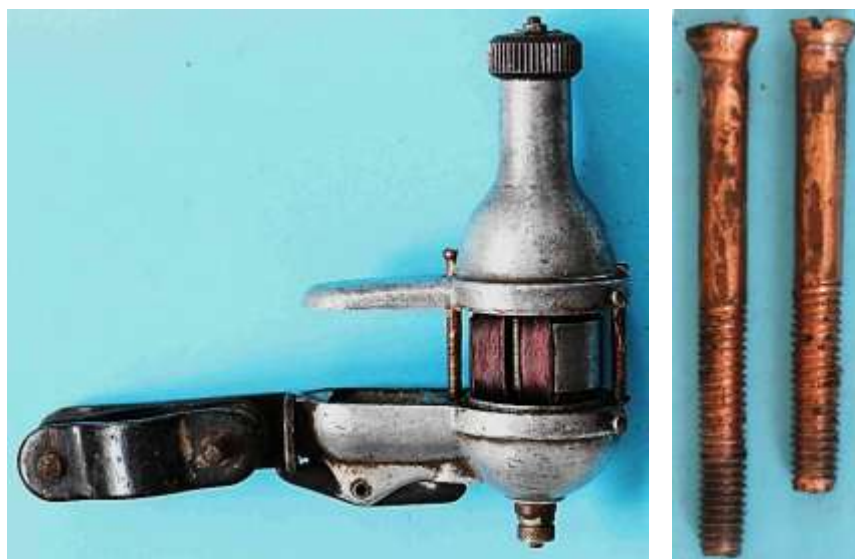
Zwei Druckgussteile mit den Messingschrauben
